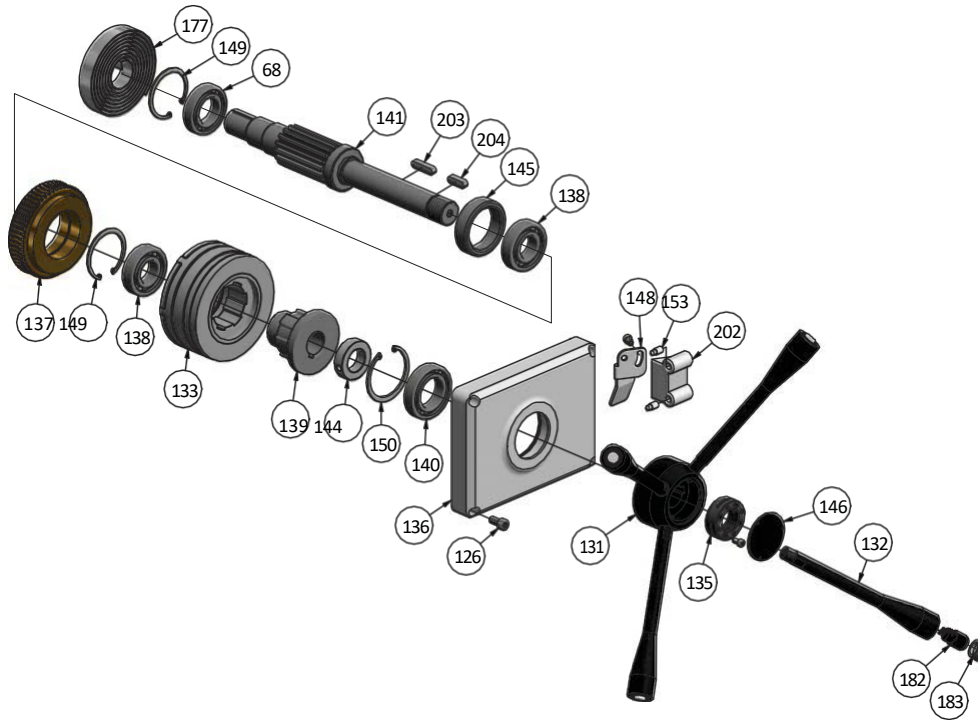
Getriebe Teil F - Section de l'engrenage F
